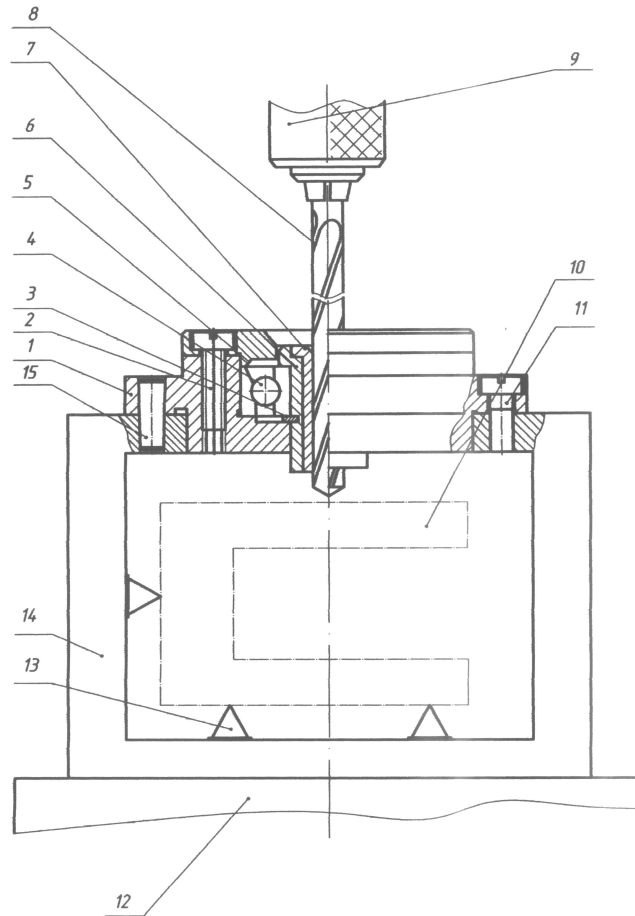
Переналагоджувальний свердлильний кондуктор [5]
